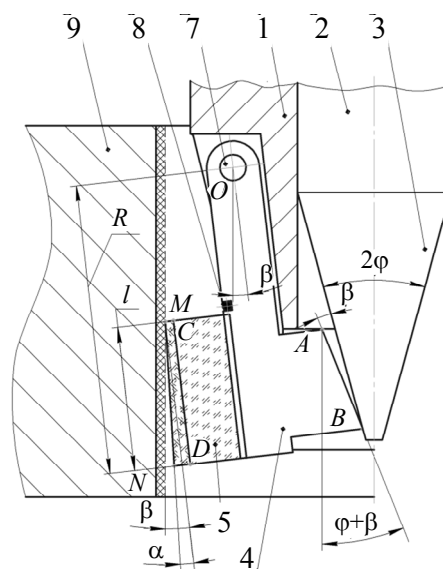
Схема взаимного расположения обрабатываемого изделия и подвижных частей инструмента, изображенного на рис.2, в момент начала съёма припуска
